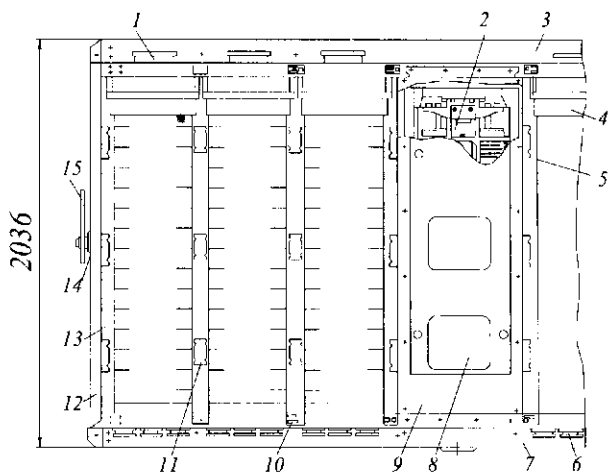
Корпус шестиприемного рессева РЗ-БРБ
